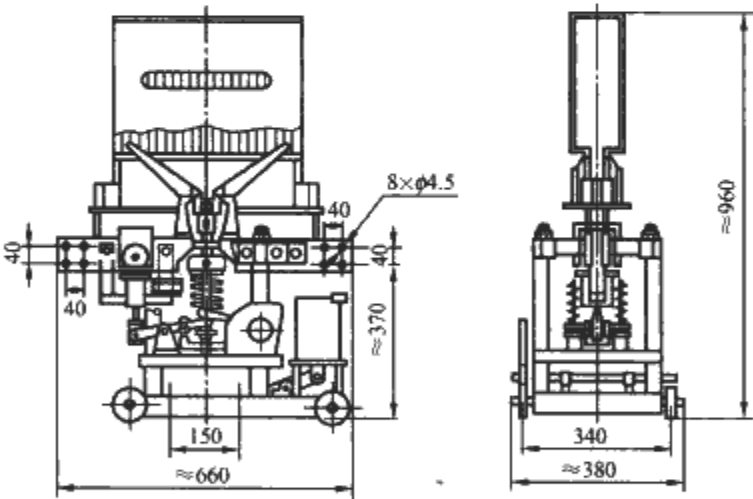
DS12-30/08 直流快速断路器的外形尺寸
